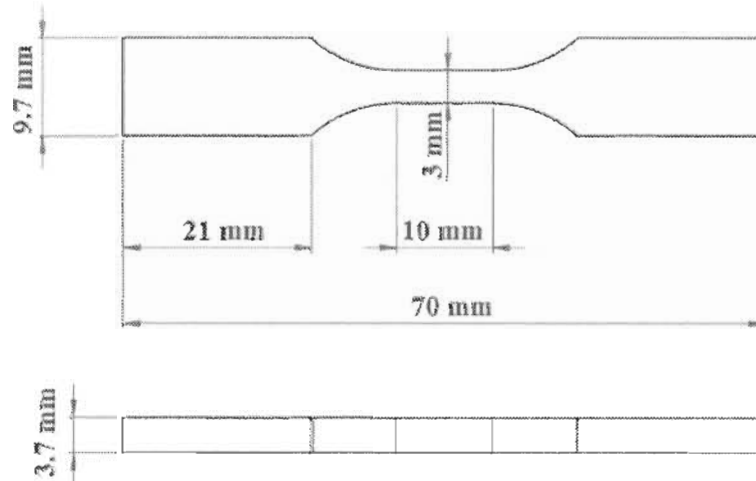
Dimensions des éprouvettes fibres/PEBD.
